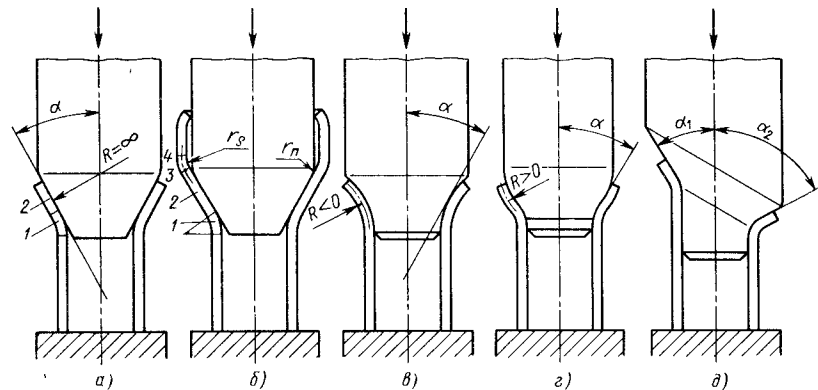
Схемы раздачи трубчатых заготовок пуансонами с различной формой рабочего участка
